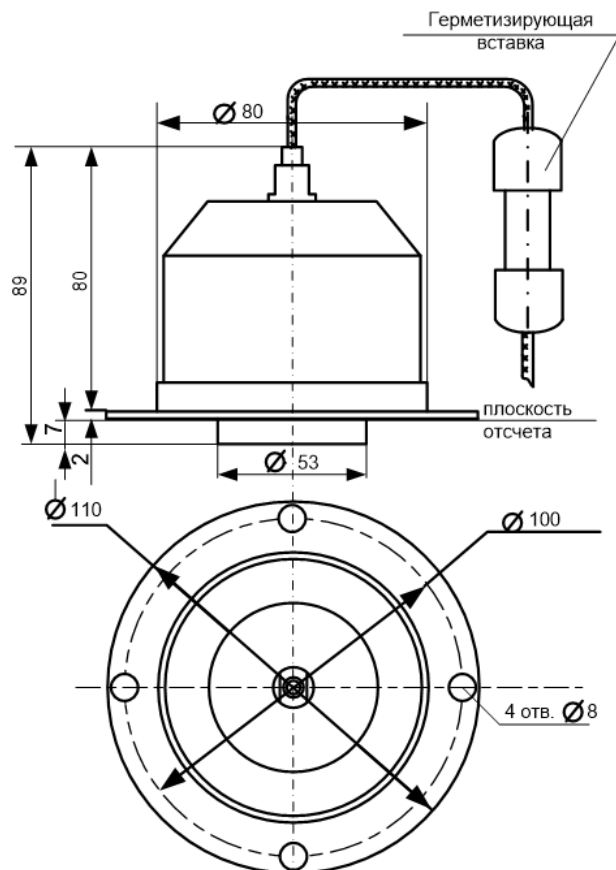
Габаритные и установочные размеры акустического преобразователя АП-13
